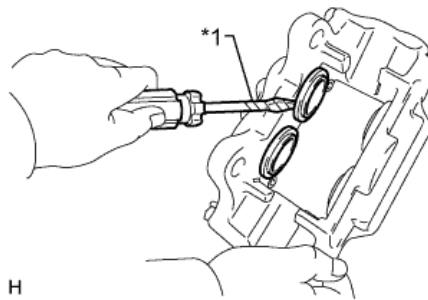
Melepas *Disc Brake Cylinder Assembly
